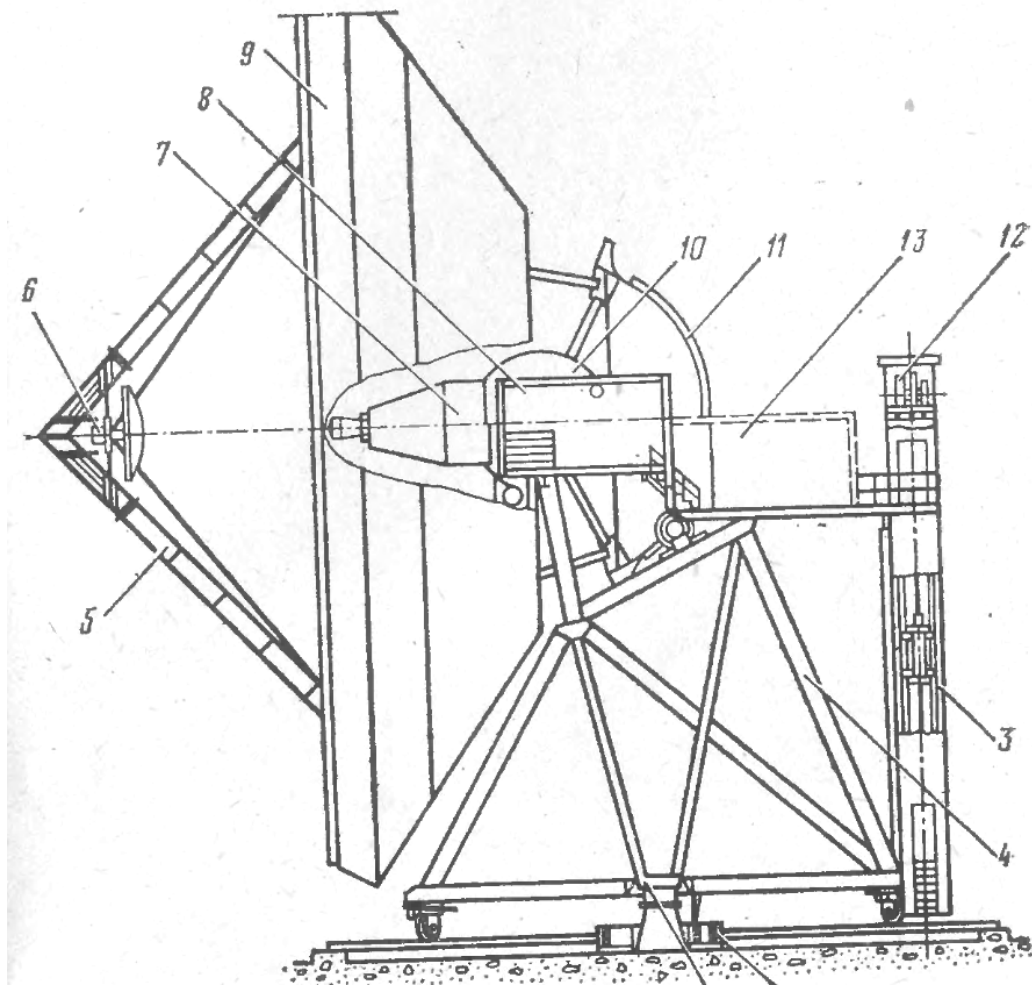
Схема опорно – поворотного пристрою з 30 метровим дзеркалом:
